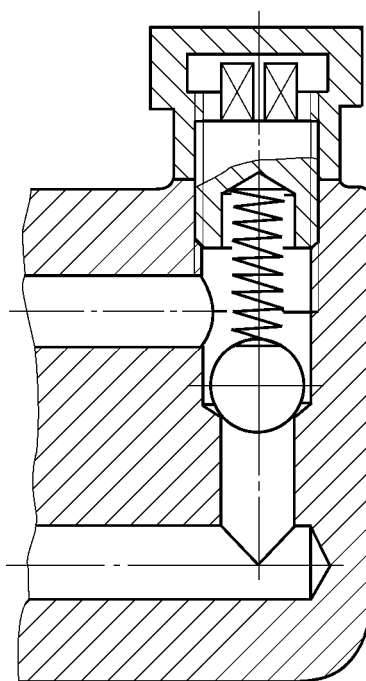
装配图中的圆柱螺旋弹簧示意画法(一)
